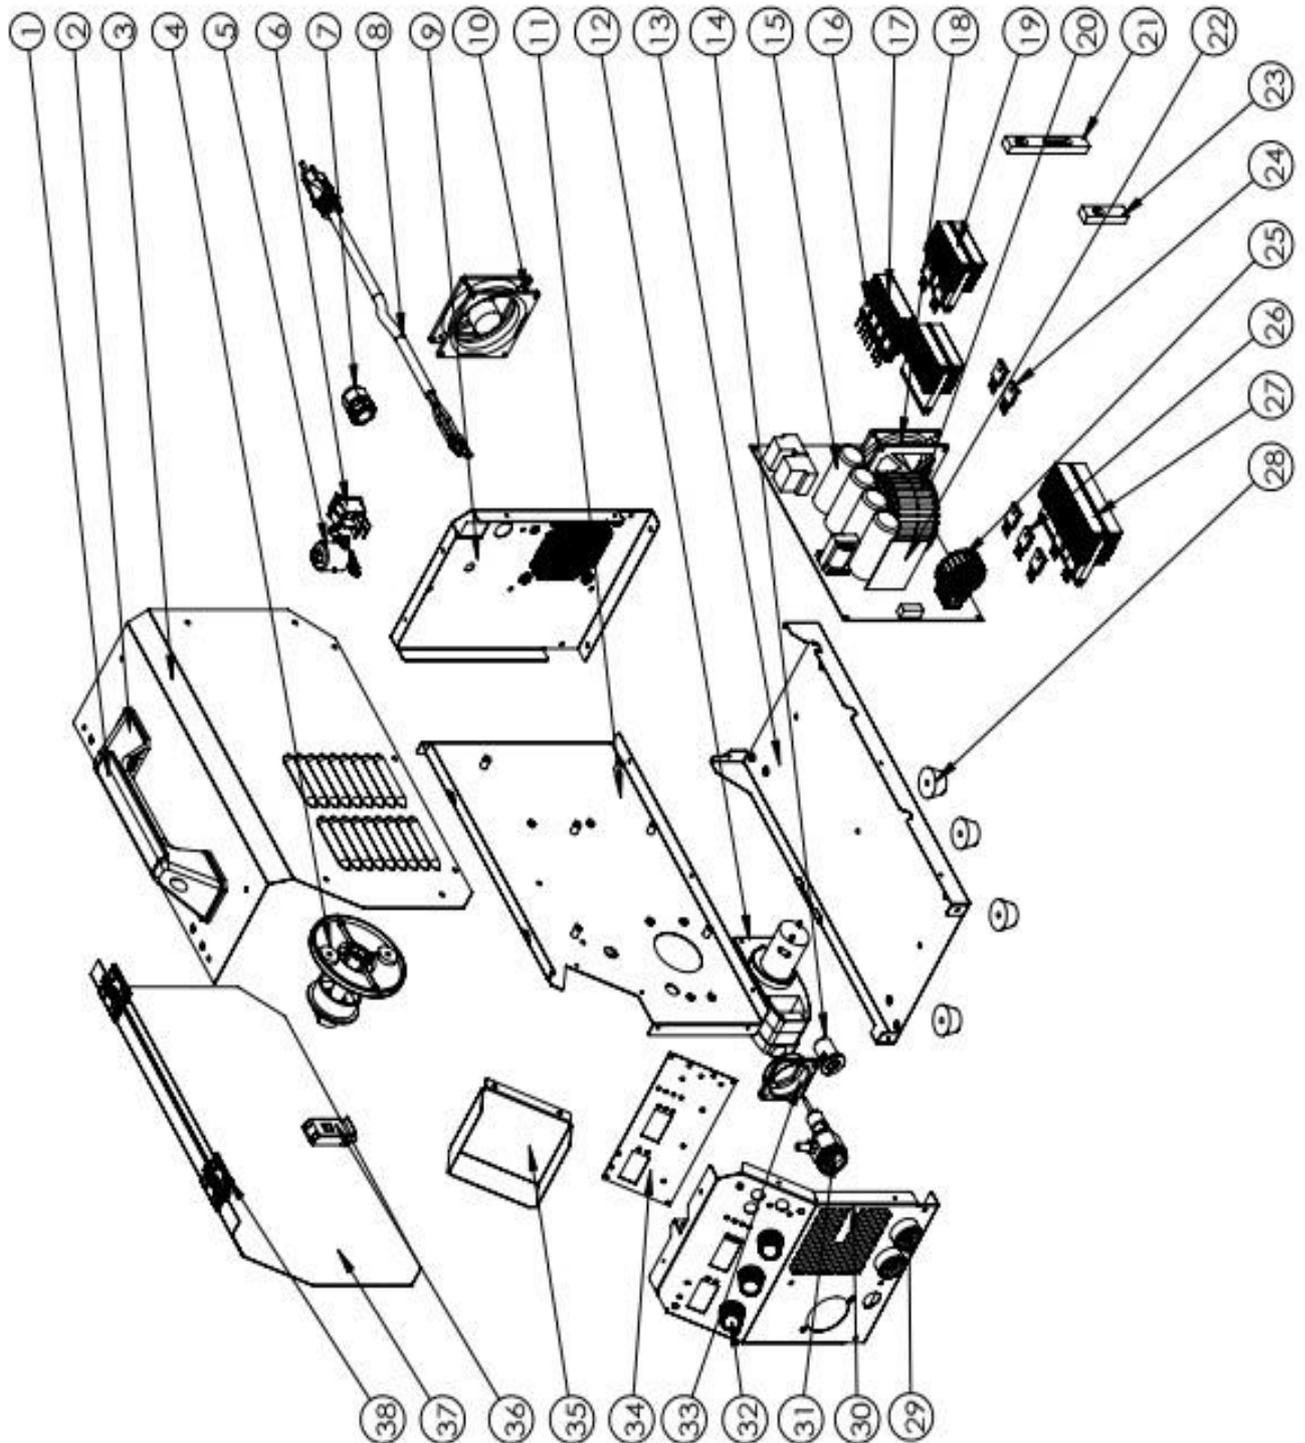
Vista explodida Easy Flex MIG 160 DV
